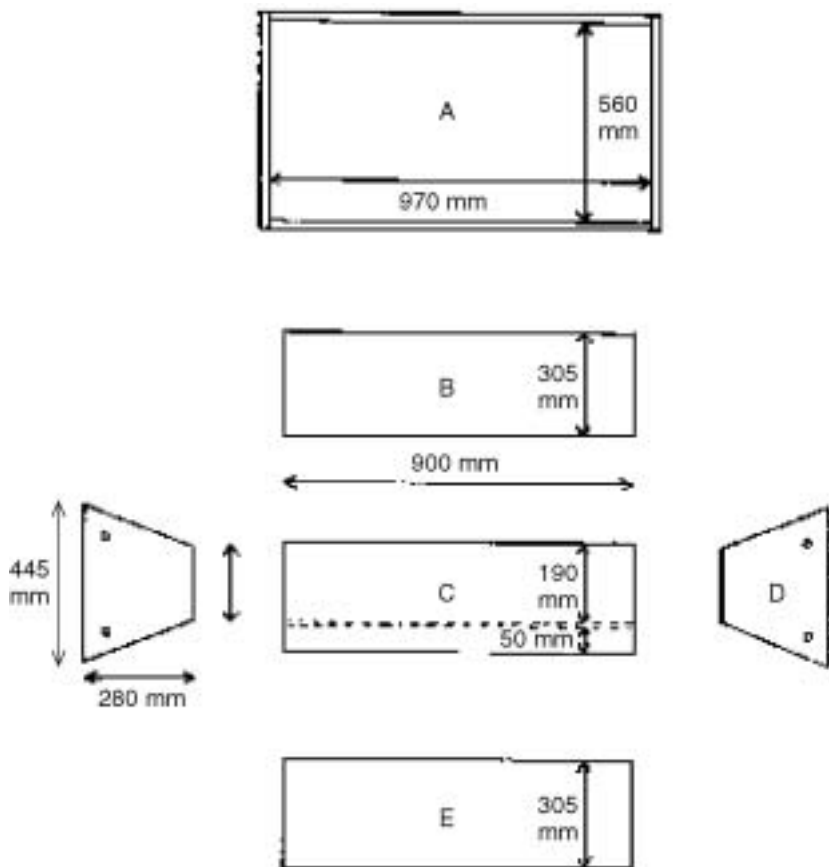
Plan d'une ruche kenyane à barrettes supérieures.
